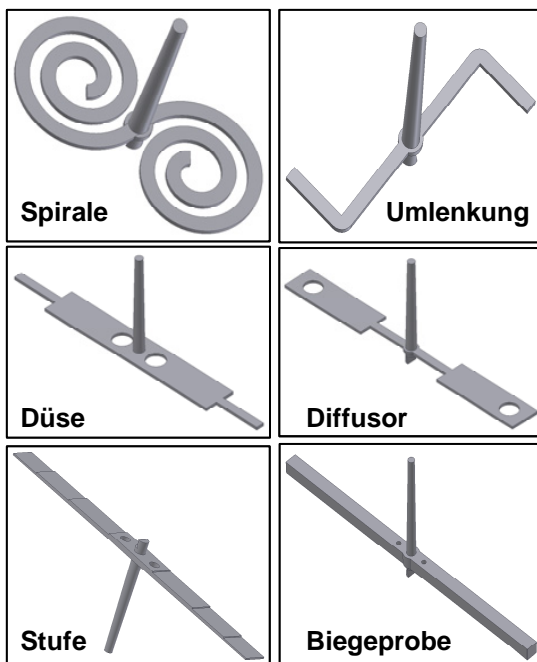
CAD-Zeichnungen der Grünlinge aus dem Probekörperwerkzeug mit Wechselformeinsätzen
